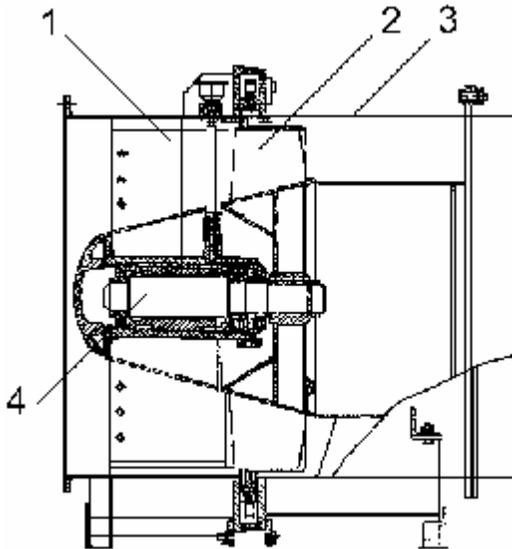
Вентилятор ВМП-6М: 1 – передняя часть корпуса; 2 – рабочее колесо с лопатками; 3 – выходная часть корпуса; 4 – вал рабочего колеса
